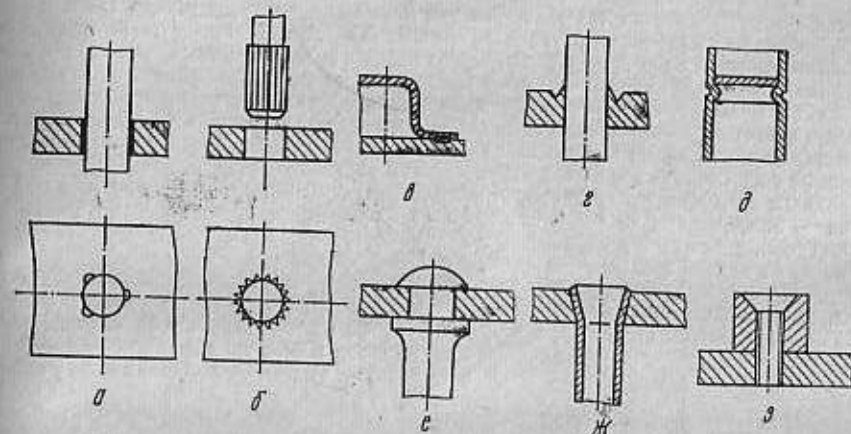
Способы закрепления элементов изделия при сборке и пайке:
